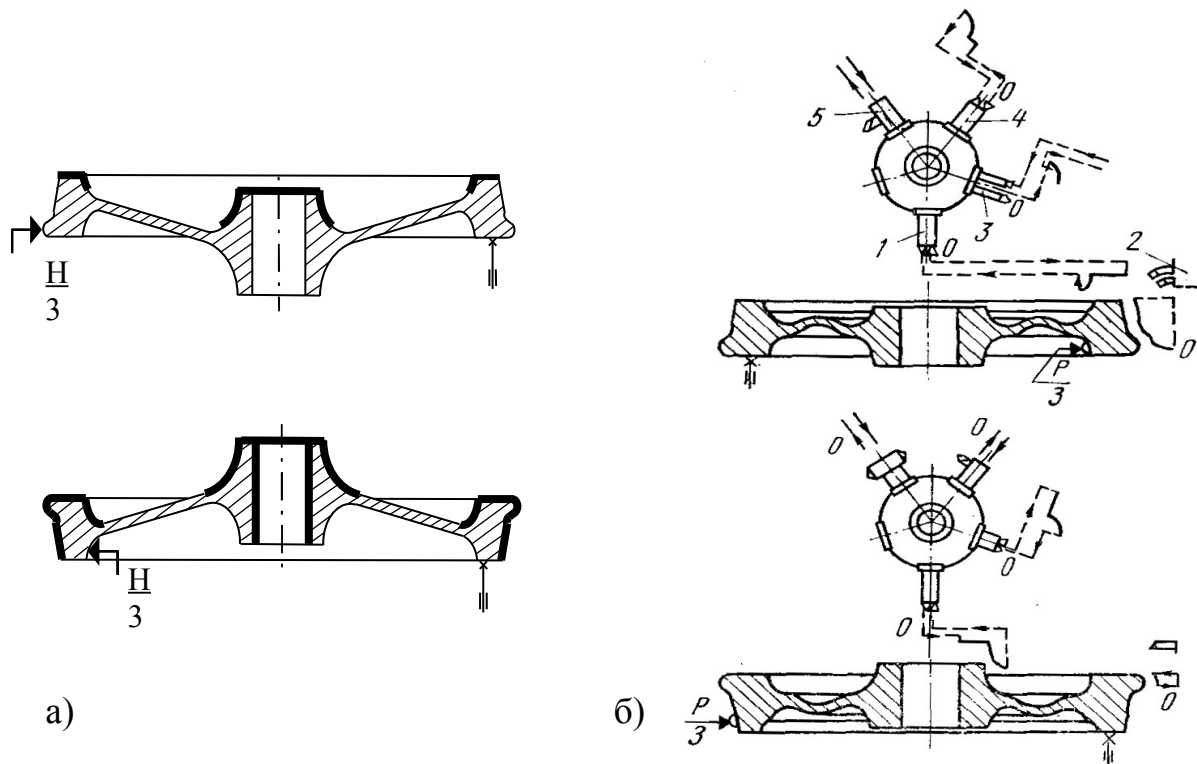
Схеми обробки колеса на верстатах: а) фірми "Kreven"(Великобританія), б) КЕ12 і КЕ14 у Німеччині
